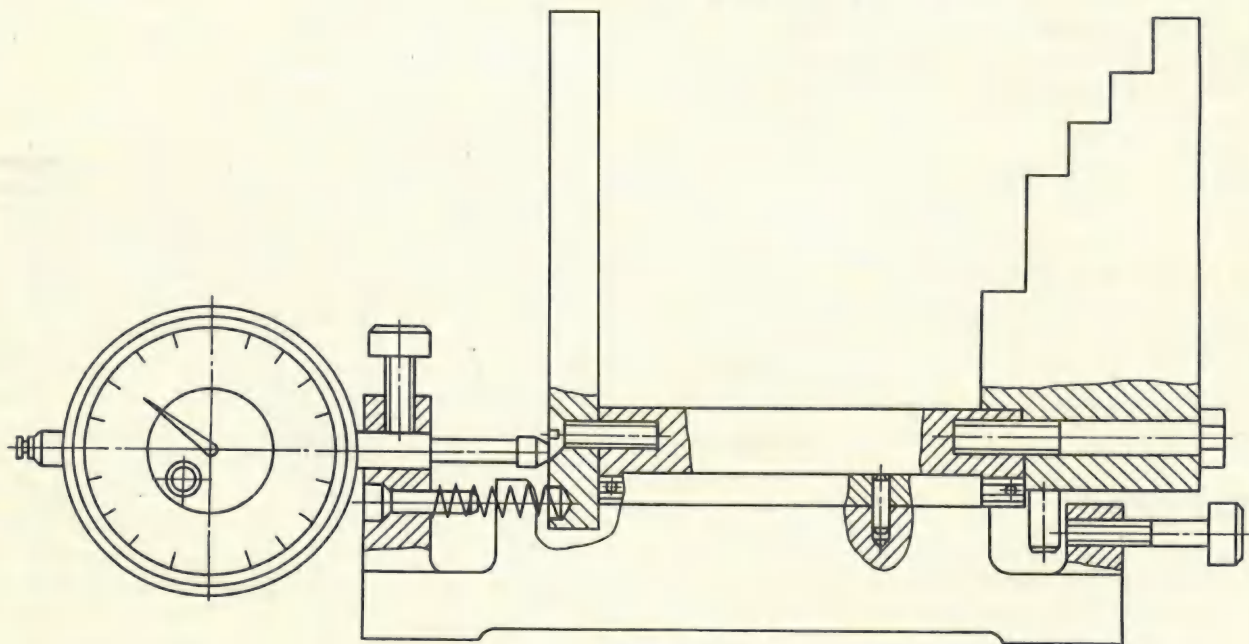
Приспособление для установки резца на шпинделе $\varnothing 78$ мм
